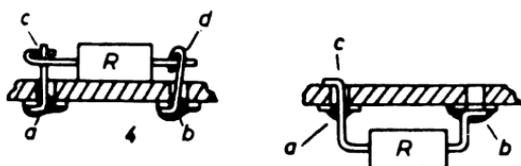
Sistemazione sopra o sotto il circuito stampato.
